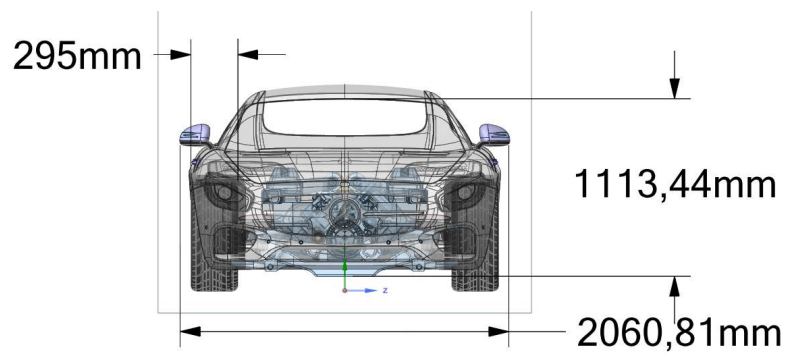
Dimensões da parte dianteira do veículo-CAD.
